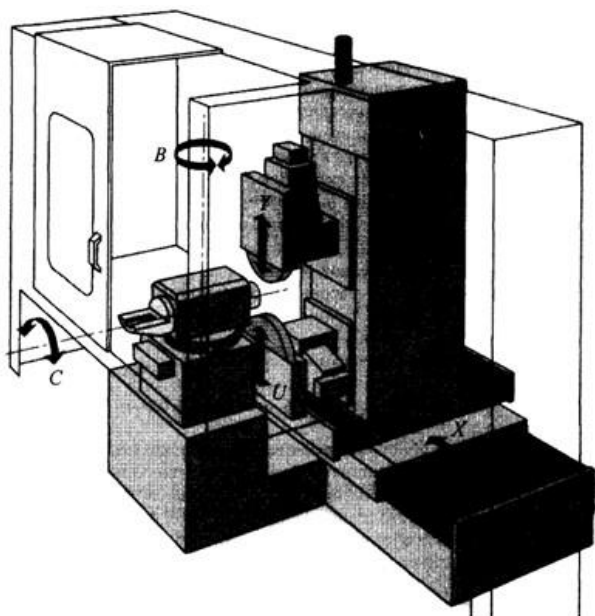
компоновна схема спеціального плоскошліфувального верстата для двобічної обробки мод. Compact-Master фірми ELB-Schliff.
